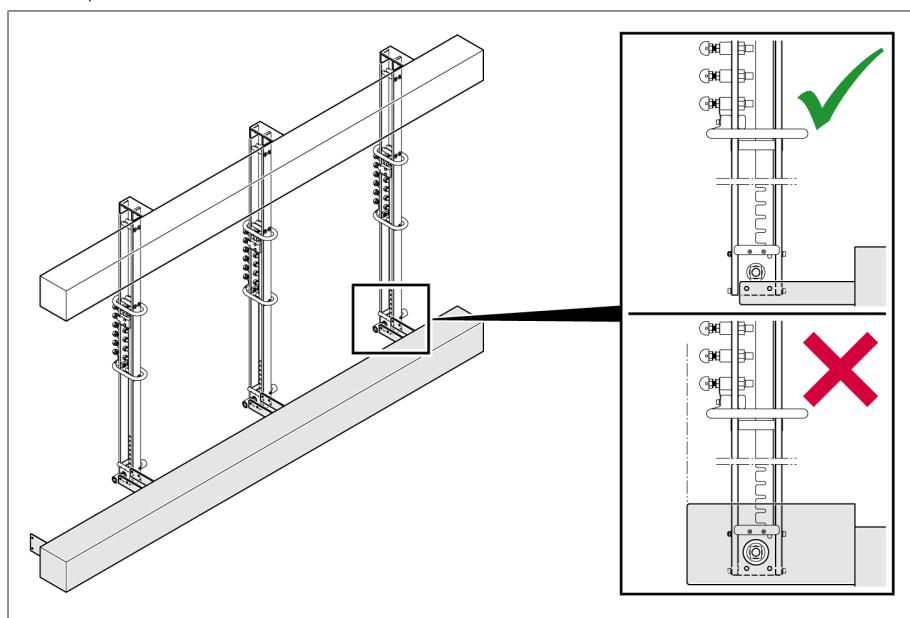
Крепежное приспособление на верхнем редукторе, устройство ПБВ с фронтальным расположением контактов
